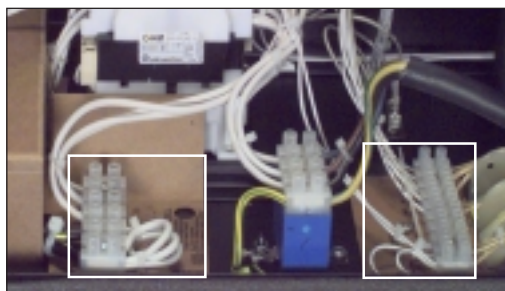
Tablette à bornes pour les transformateurs de soudage et de commande
